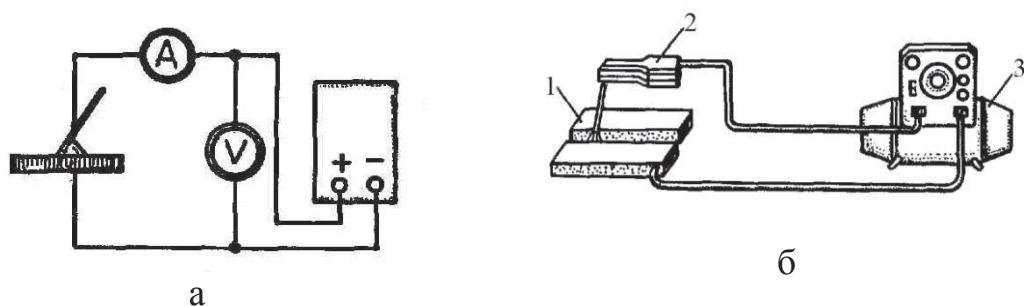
Схема процесса ручной дуговой сварки с покрытыми электродами
